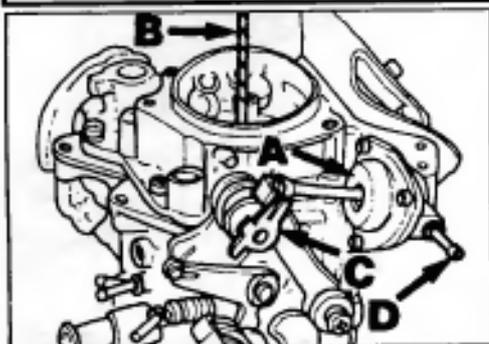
Зазор воздушной заслонки и пусковое устройство
